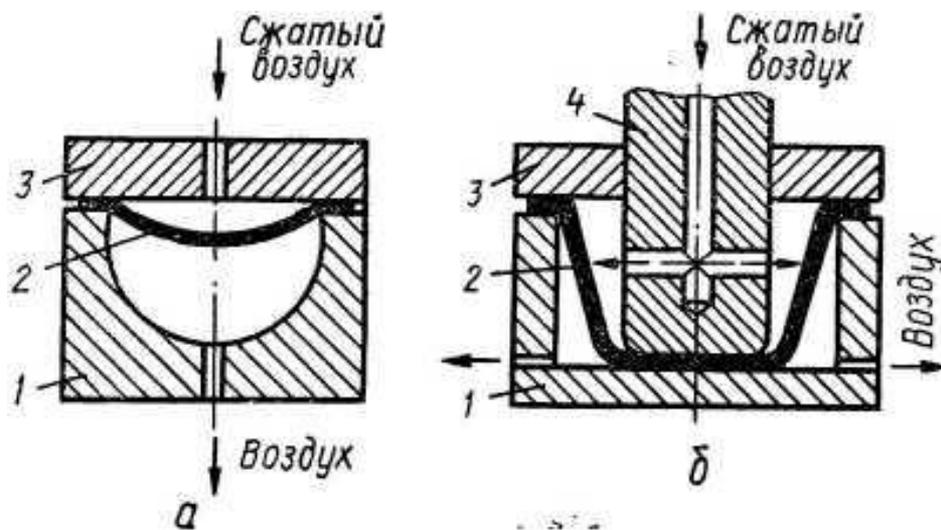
Схема дутьевого формования: а – негативного; б – позитивного; 1 – матрица; 2 – заготовка в процессе формования; 3 – прижимная плита; 4 – пуансон
